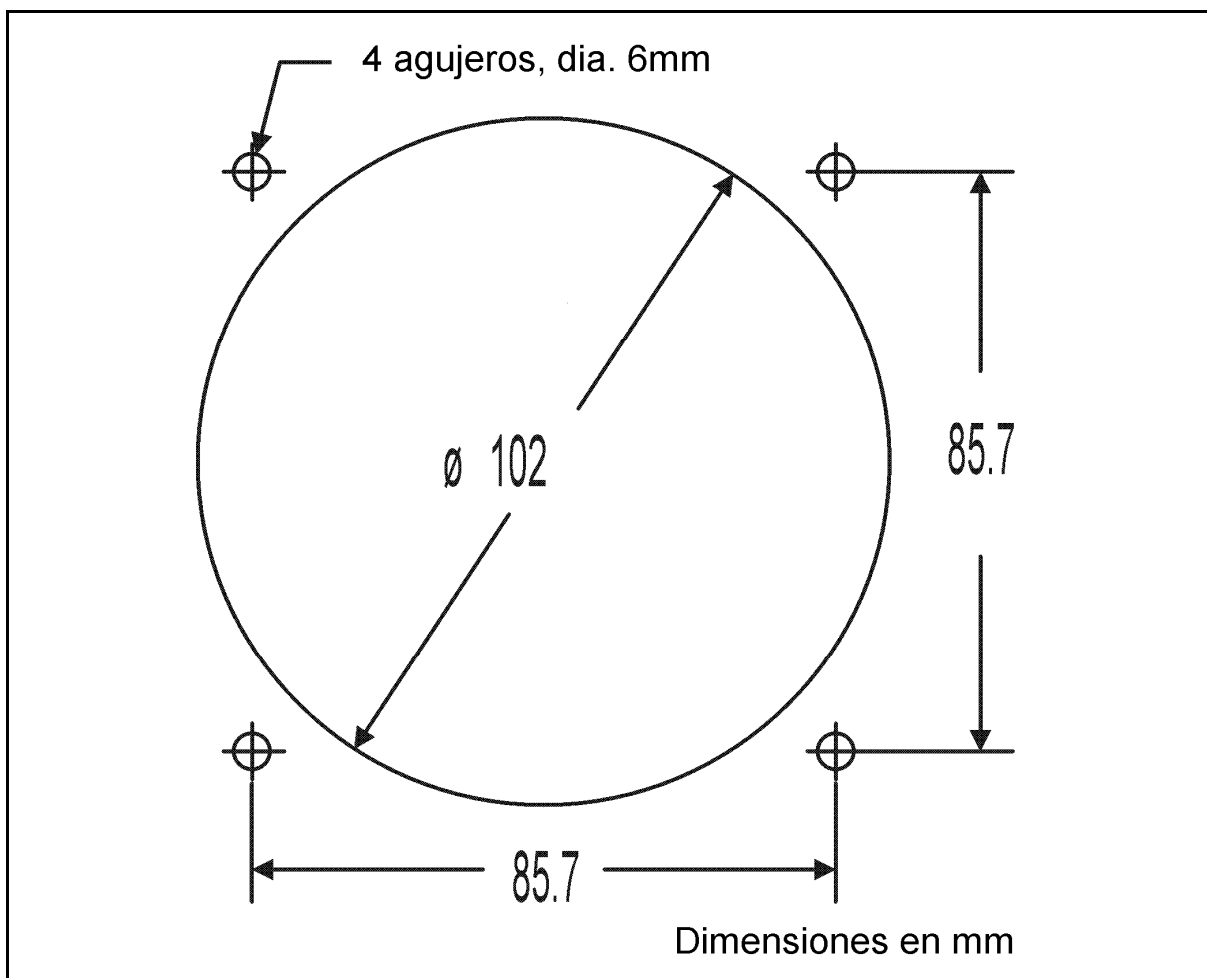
DIMENSIONES DEL CORTE DEL PANEL
